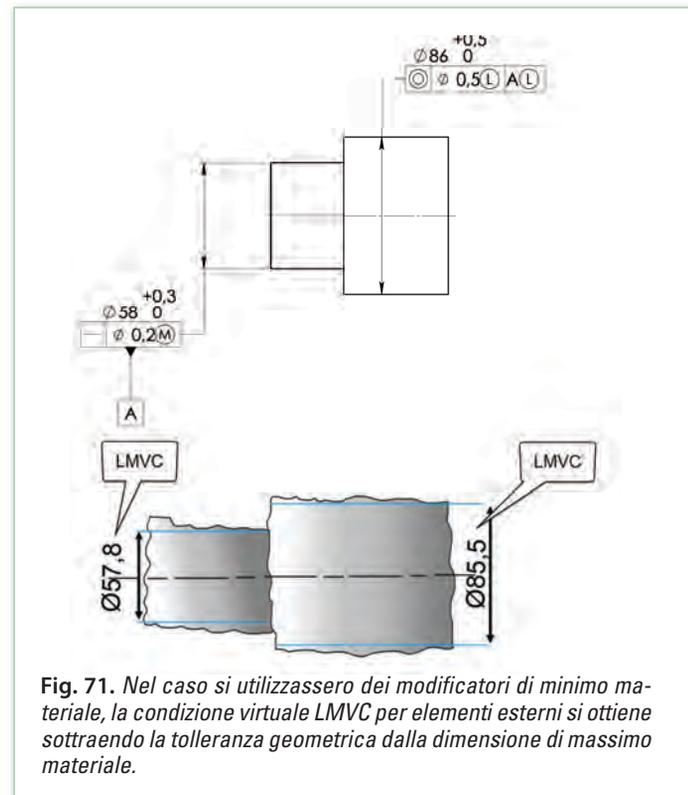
Nel caso si utilizzassero dei modificatori di minimo materiale, la condizione virtuale LMVC per elementi esterni si ottiene sottraendo la tolleranza geometrica dalla dimensione di massimo materiale.
